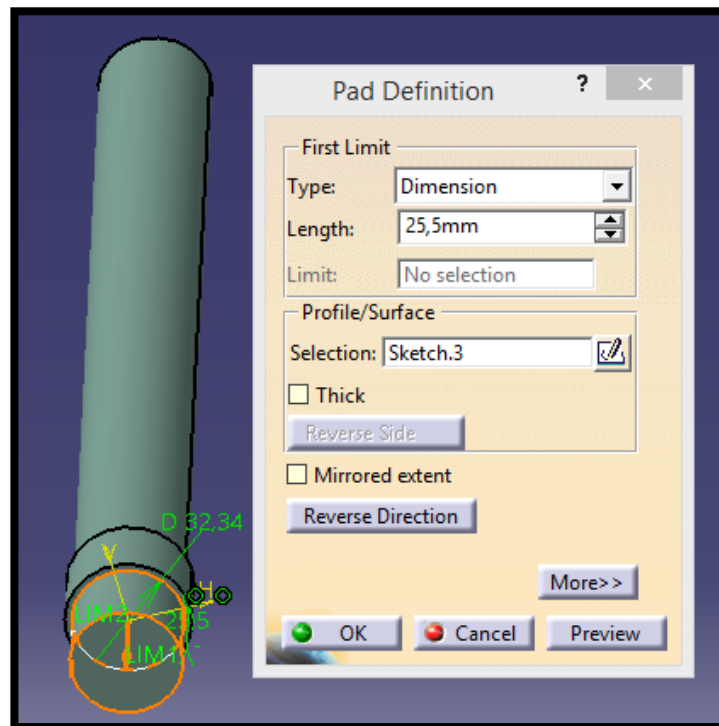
Seat mounting frame 11: Pad.3 barra inferior 2
